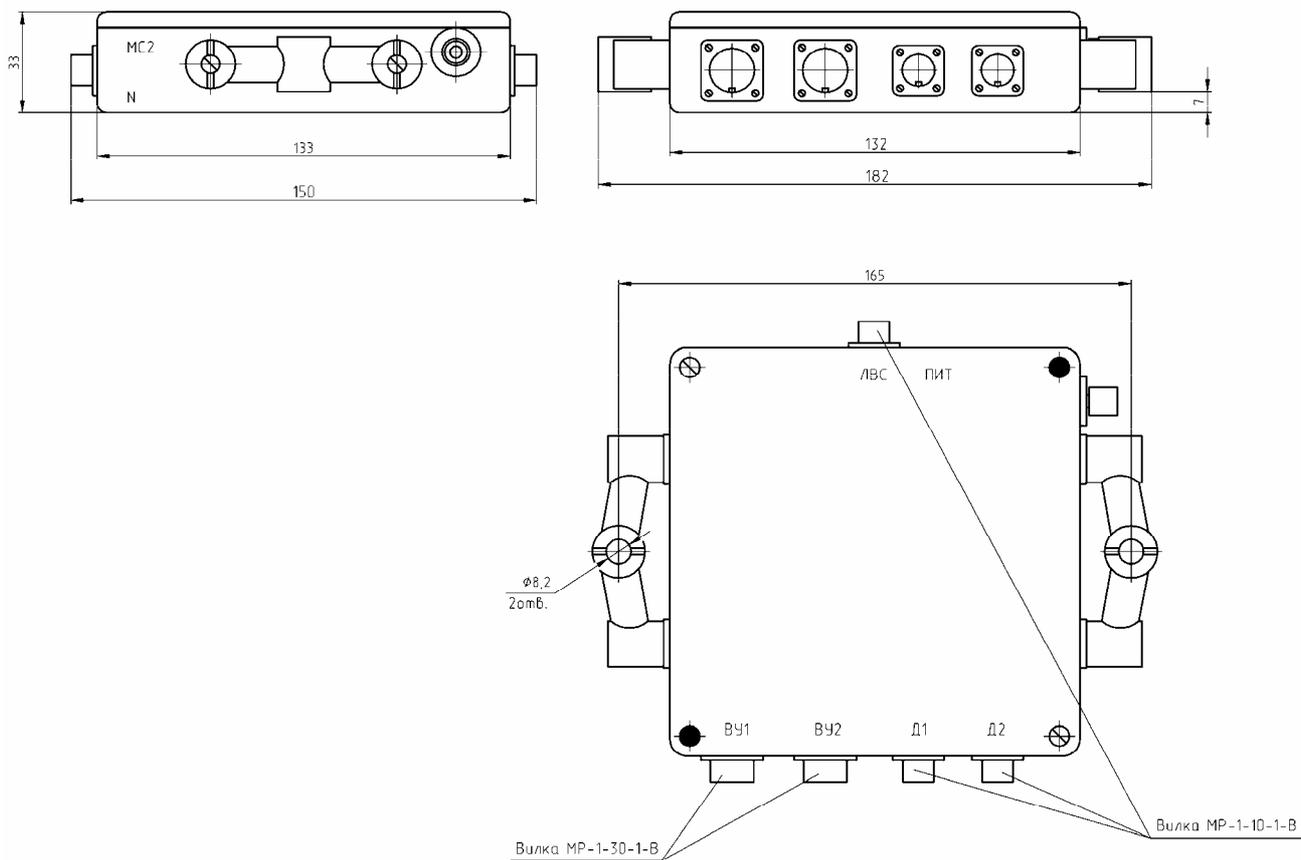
Габаритные чертеж блока сопряжения МС2
